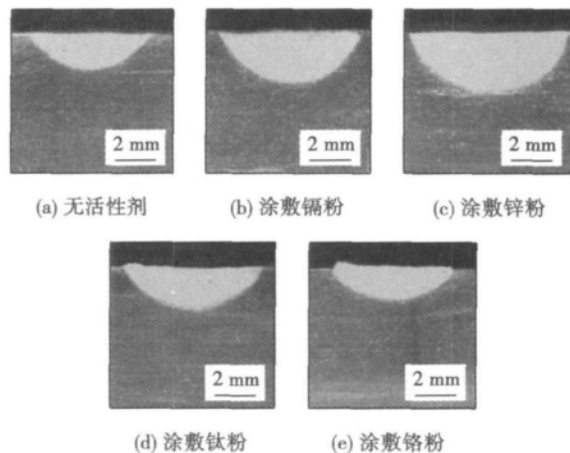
未涂敷和涂敷活性剂的焊缝横截面形貌
